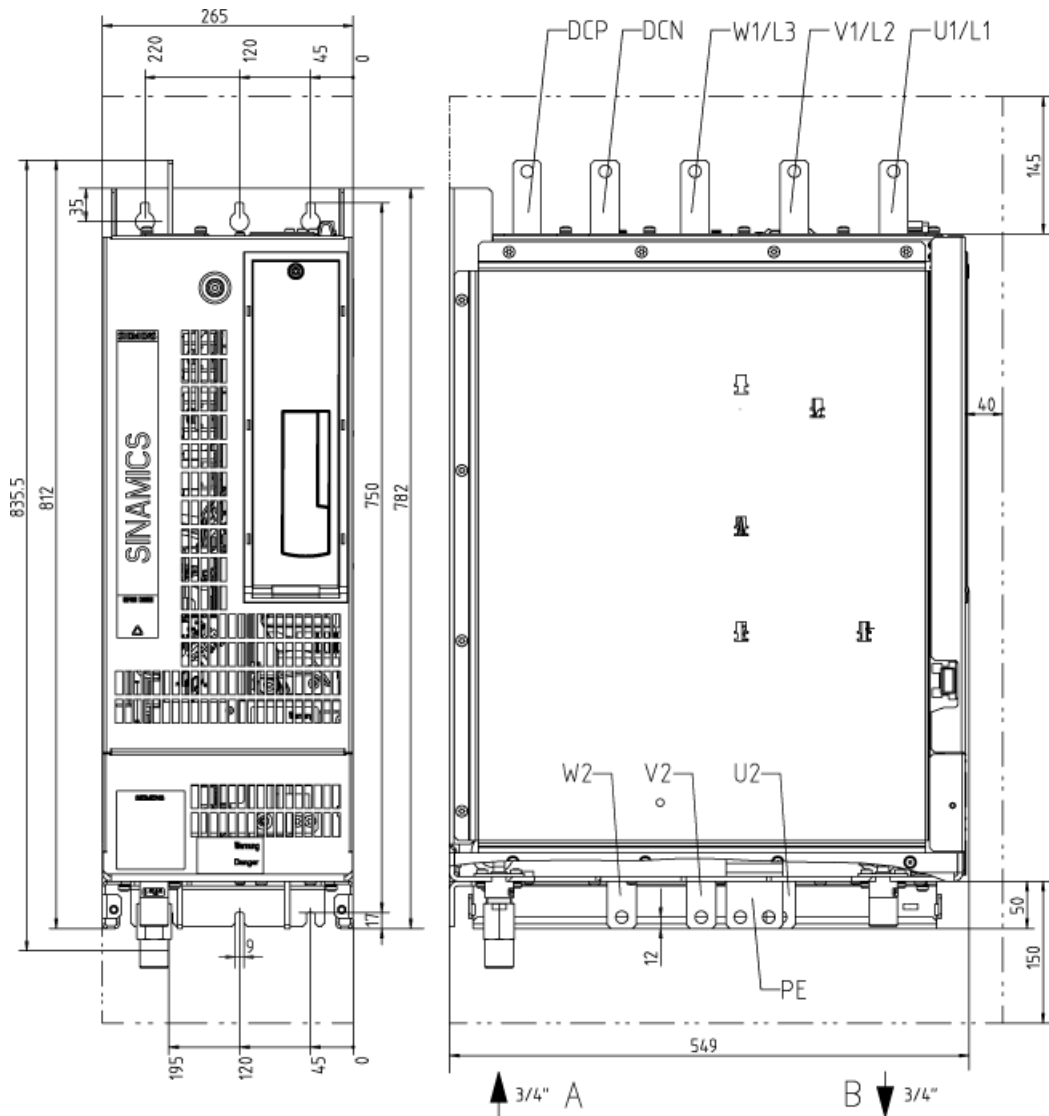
Габаритный чертёж силового модуля, типоразмер FL. Вид спереди, вид сбоку
